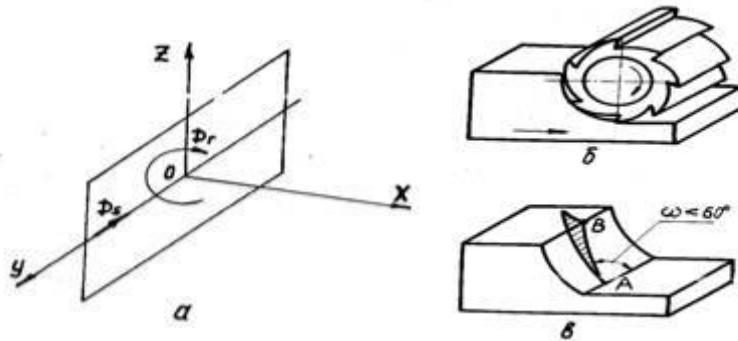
Схема традиционного цилиндрического фрезерования инструментом с винтовыми зубьями
